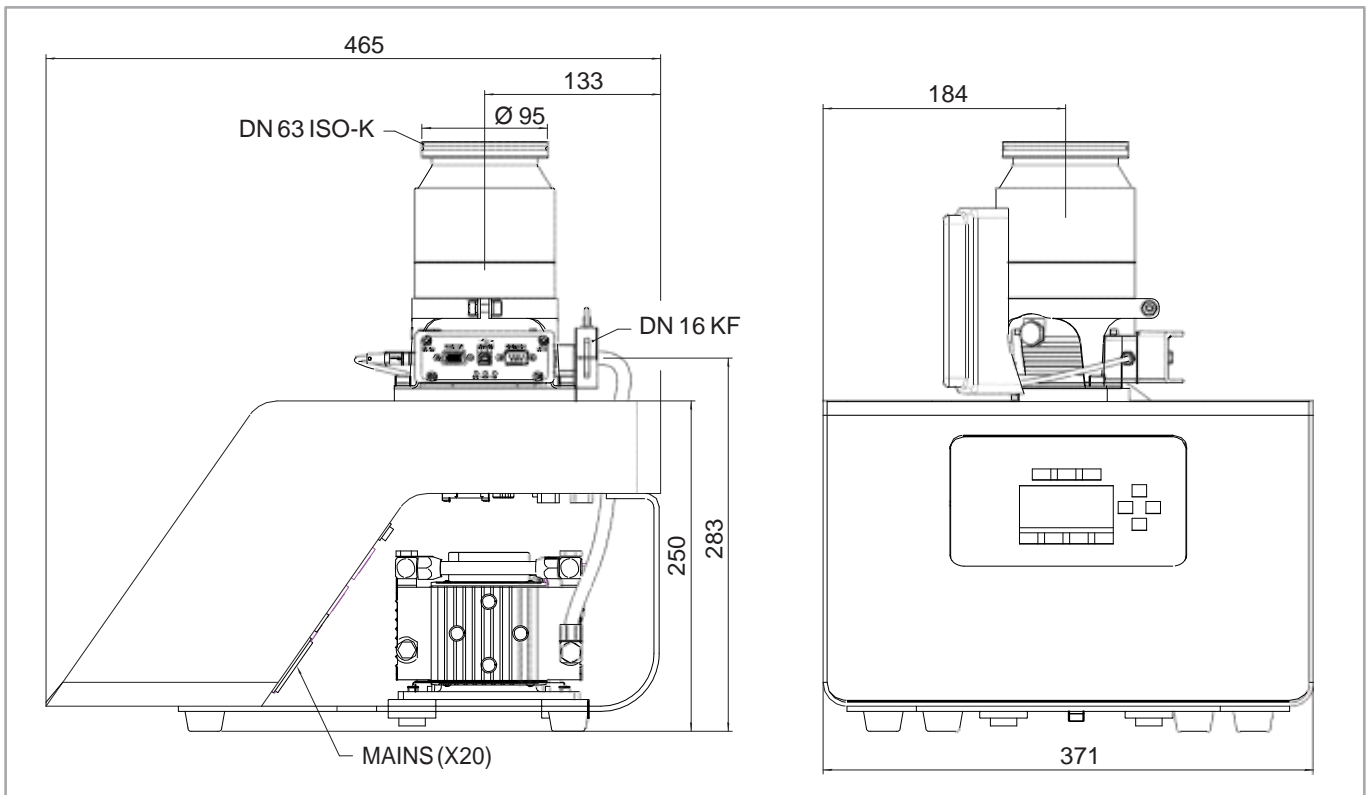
Габаритные размеры TURBOLAB 90, размеры в мм
